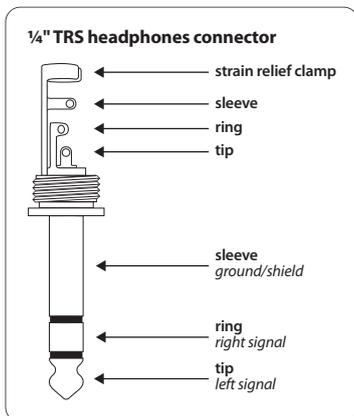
cablatura di una spina jack stereo per cuffia e della spina jack stereo per il CD INPUT
